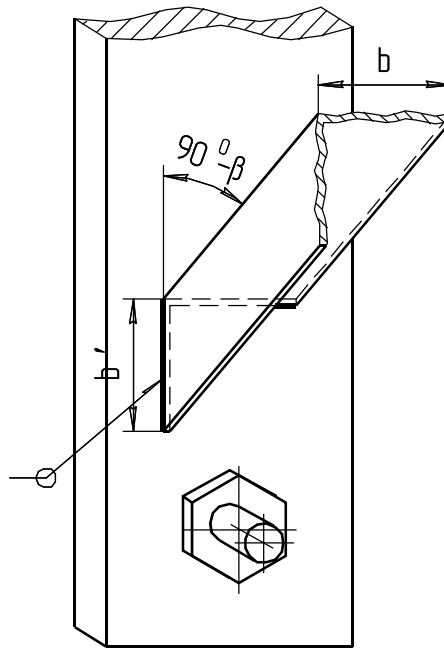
Схема сварного шва крепления подкоса к стойке
